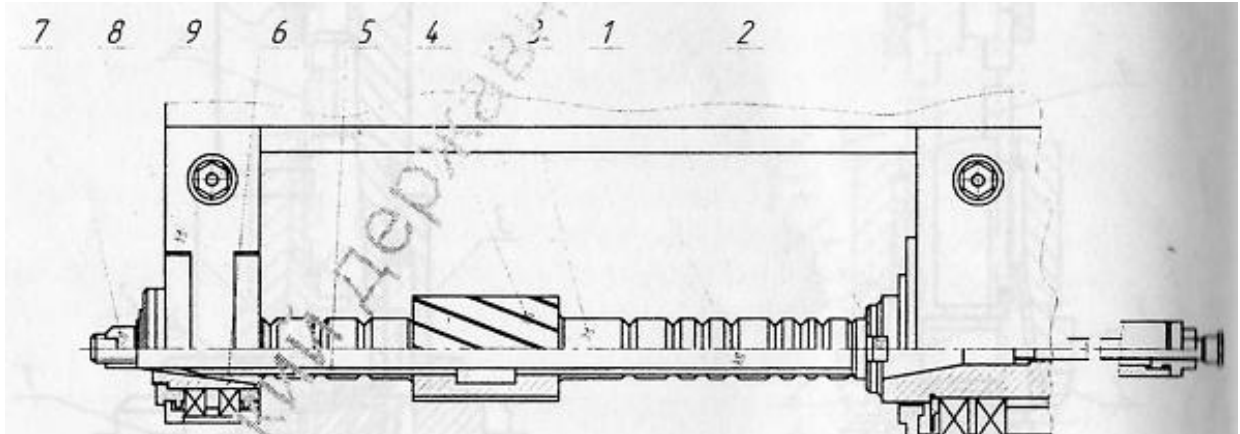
Схема закріплення фрези на горизонтально-фрезерувальному верстаті
